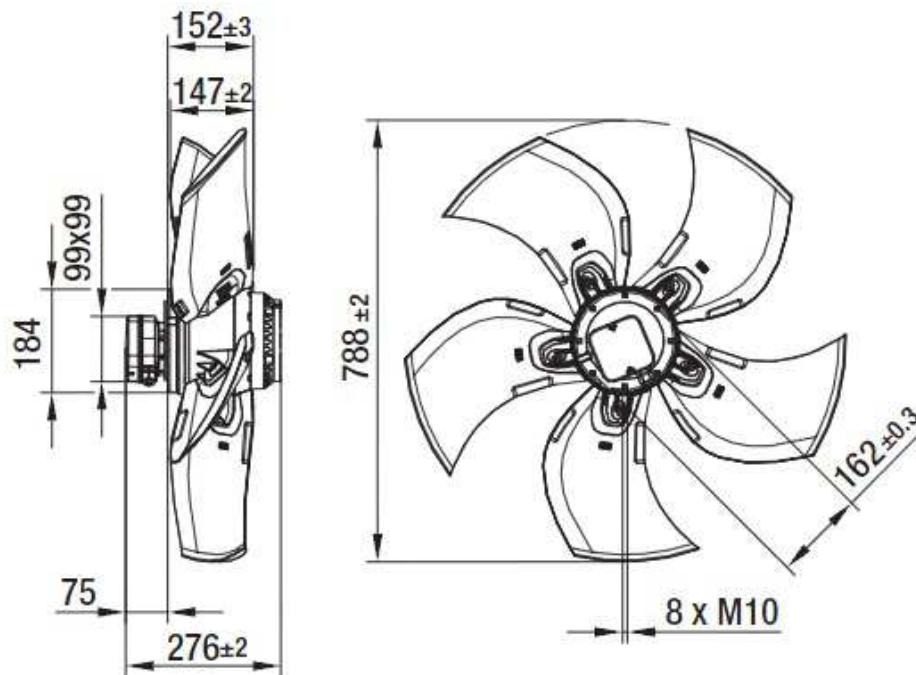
disegno CAD ventilatore A6D800-AD01-01
